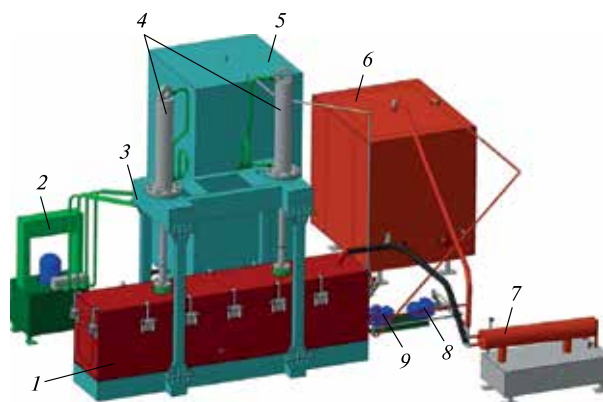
3D-модель сушильно-прессовой установки СПК-1М: 1 — рабочая ванна; 2 — рама; 3 — гидростанция; 4 — гидроцилиндры; 5 — емкость для холодного антисептика; 6 — емкость для горячего антисептика; 7 — теплообменник; 8 — насосный агрегат для перекачки горячего антисептика; 9 — насосный агрегат для перекачки холодного антисептика
